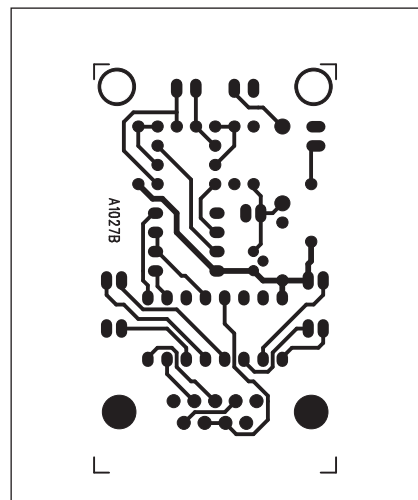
Obrazec desky spojů konvertoru (strana TOP)
